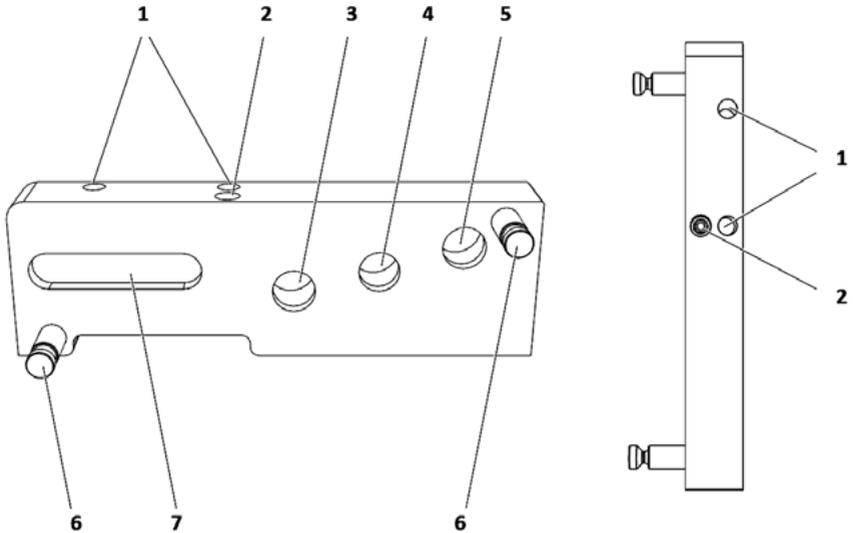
Endplatte rechts mit Gewinde für Anschluss 1, 3, 5 (REF-EPR-02)
